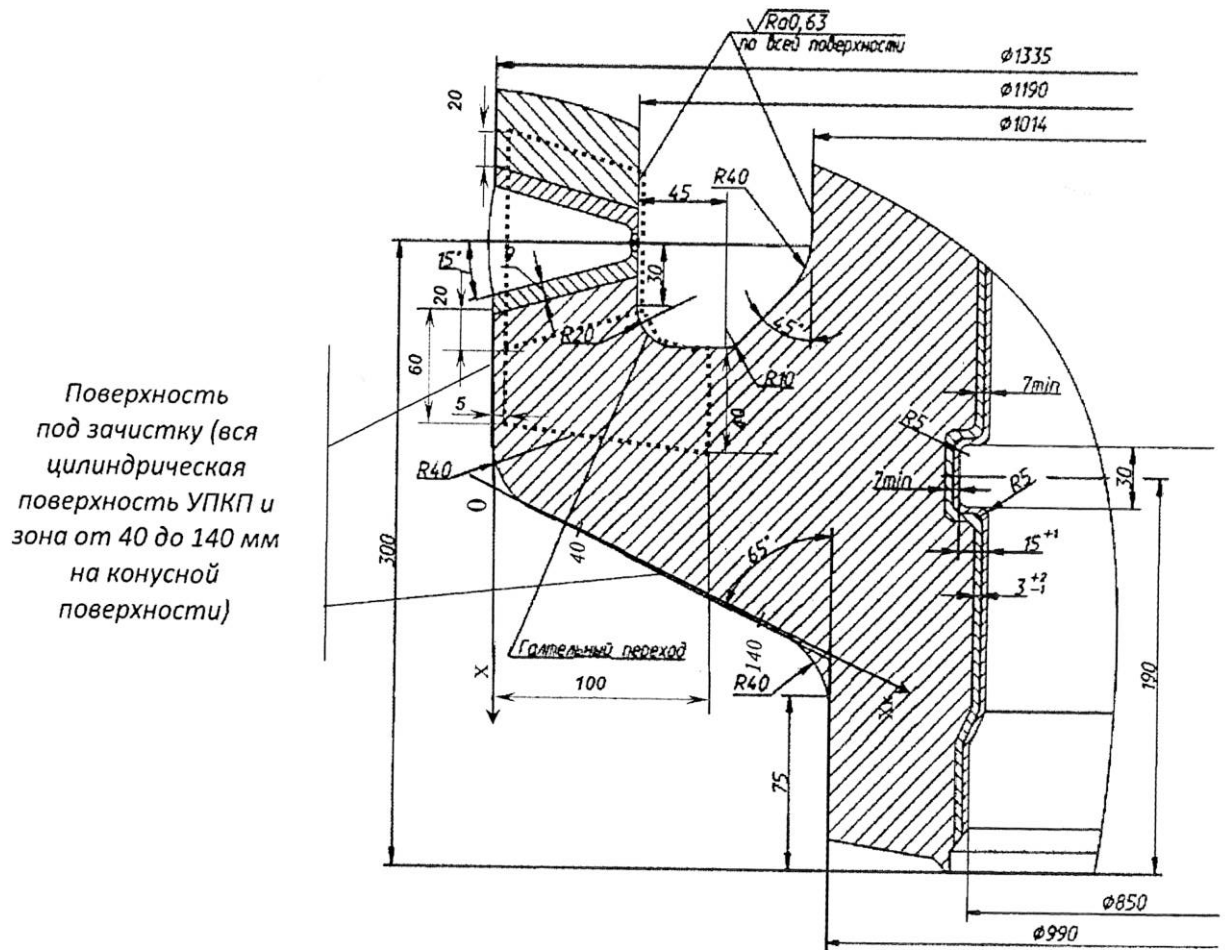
Эскиз сварного соединения с симметричной разделкой, пунктиром обозначена область контроля
